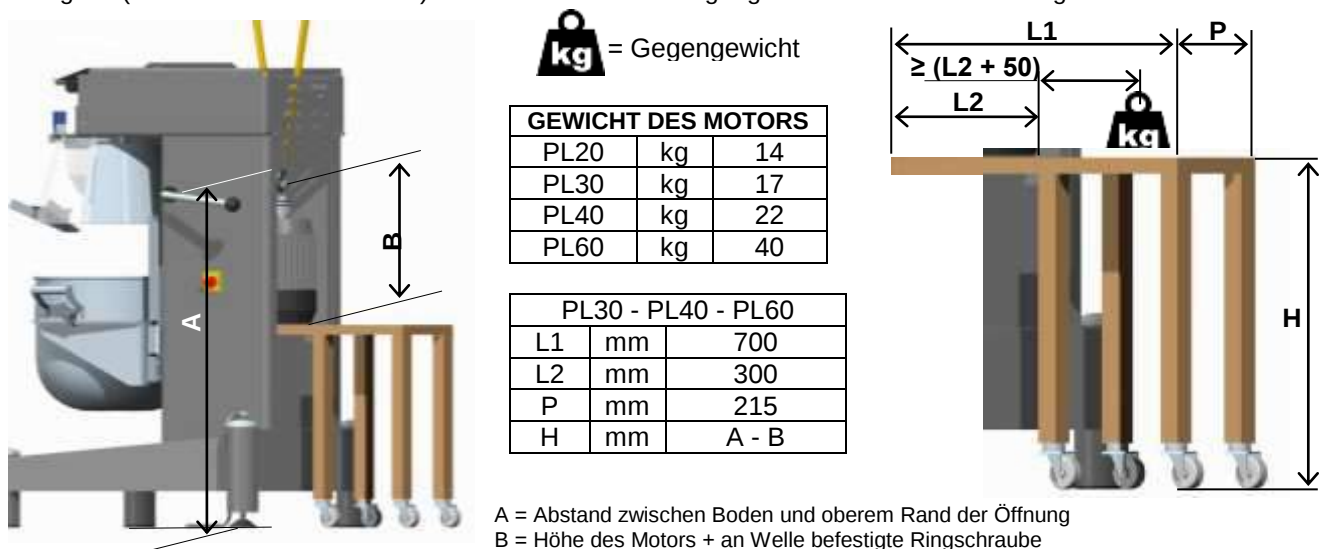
Hilfsmittel für die Montage/Demontage des Werkzeug-Motors
